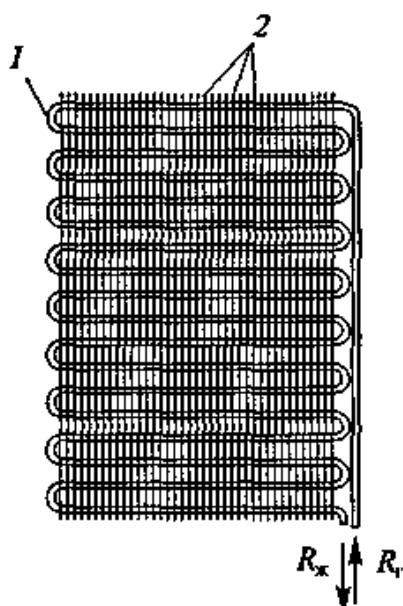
Змеевиковый конденсатор с проволочными ребрами:
